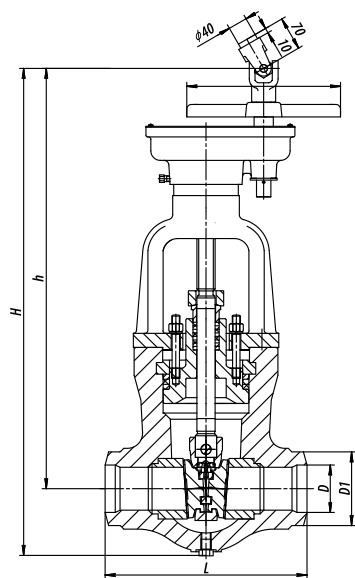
Задвижка DN100 с цилиндрическим редуктором
